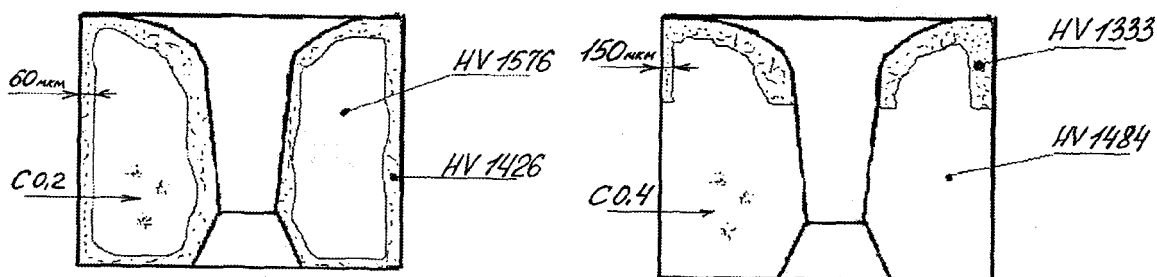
Твердосплавные волокни-заготовки с износостойким упрочненным покрытием
